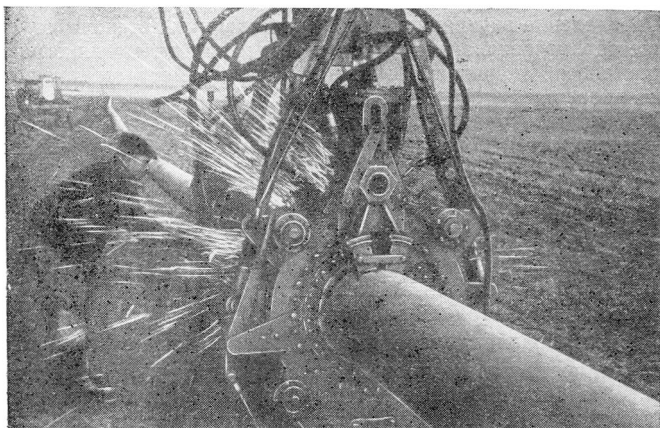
Общий вид агрегата контактной сварки труб.
